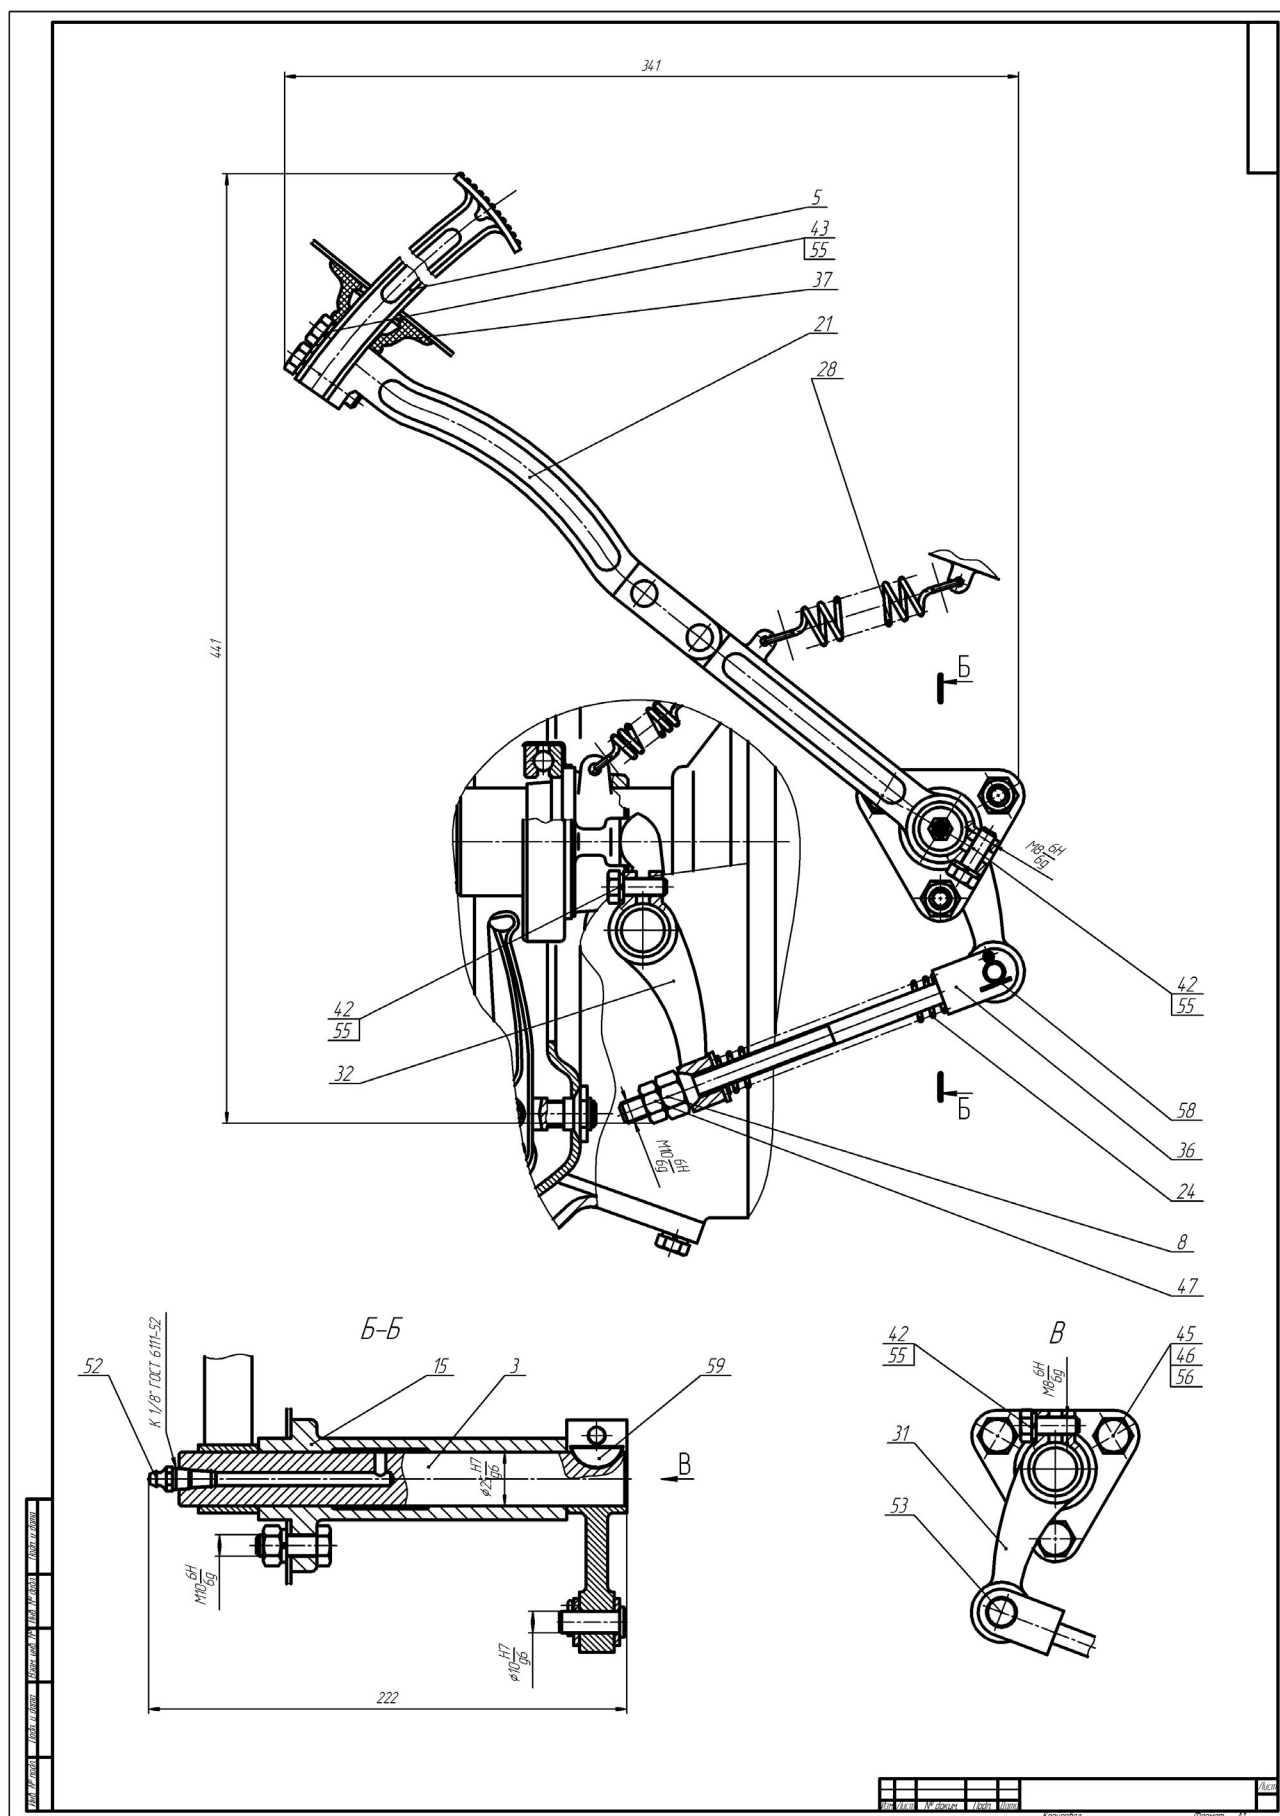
Пример выполнения сборочного чертежа сцепления
